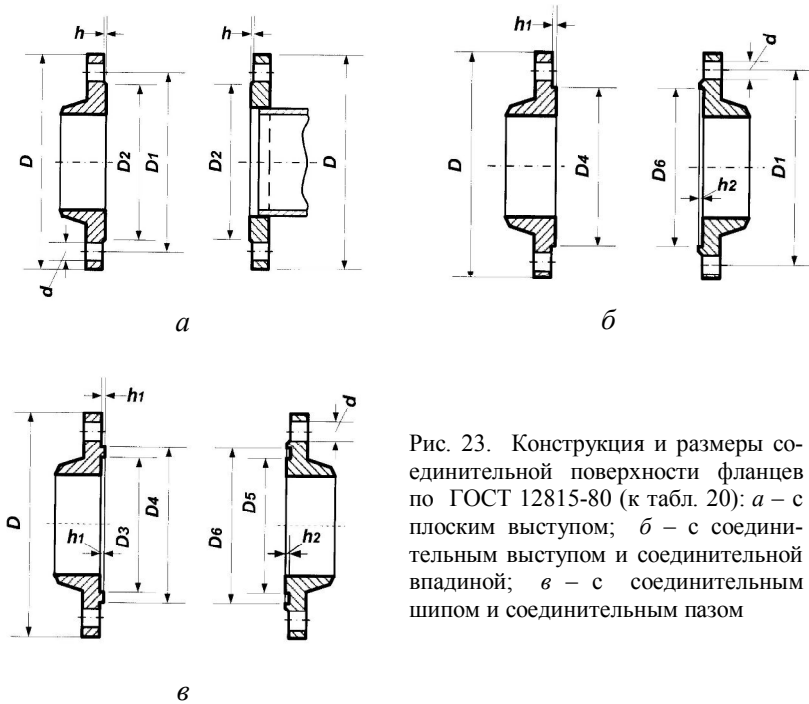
Конструкция и размеры соединительной поверхности фланцев по ГОСТ 12815-80 (к табл. 20): а – с плоским выступом; б – с соединительным выступом и соединительной впадиной; в – с соединительным шипом и соединительным пазом
